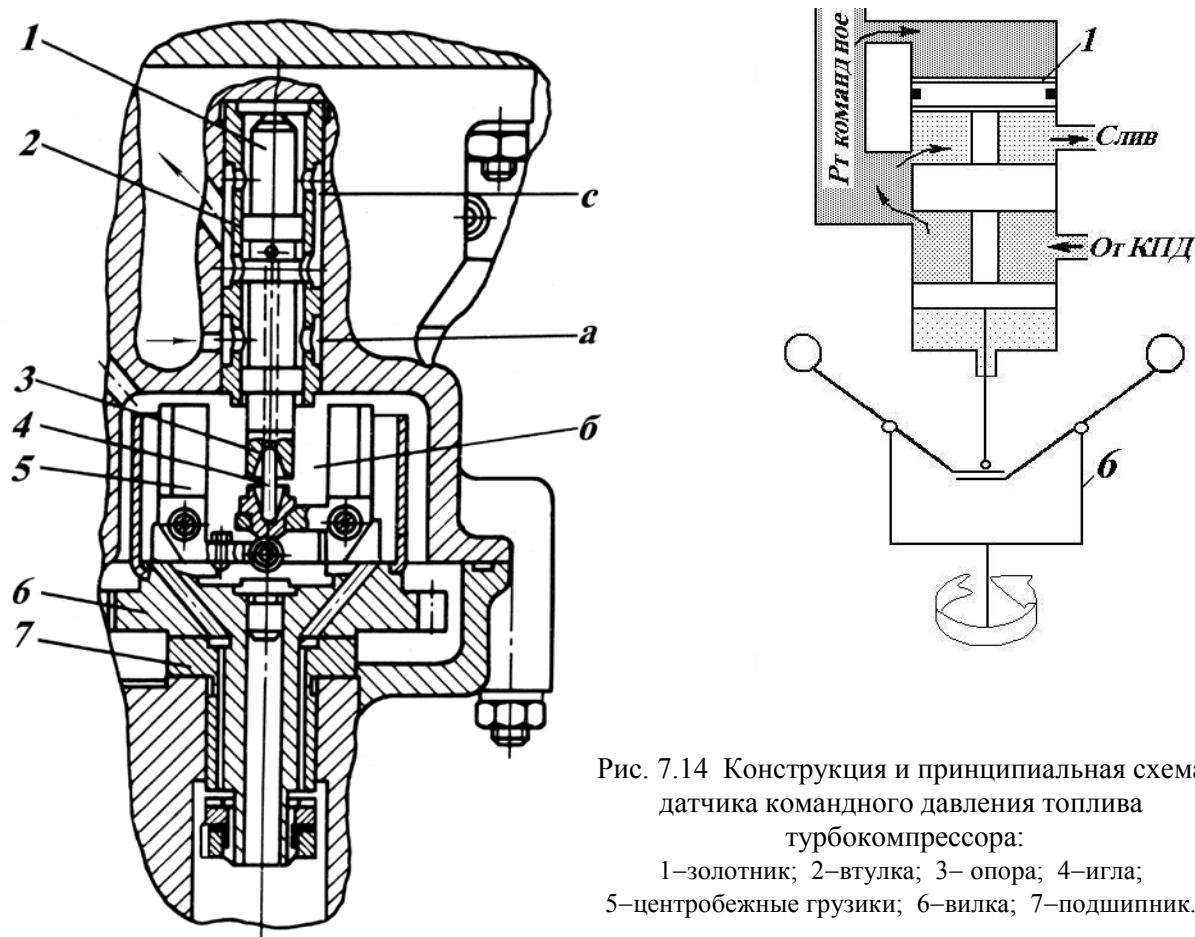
Конструкция и принципиальная схема датчика командного давления топлива турбокомпрессора:
